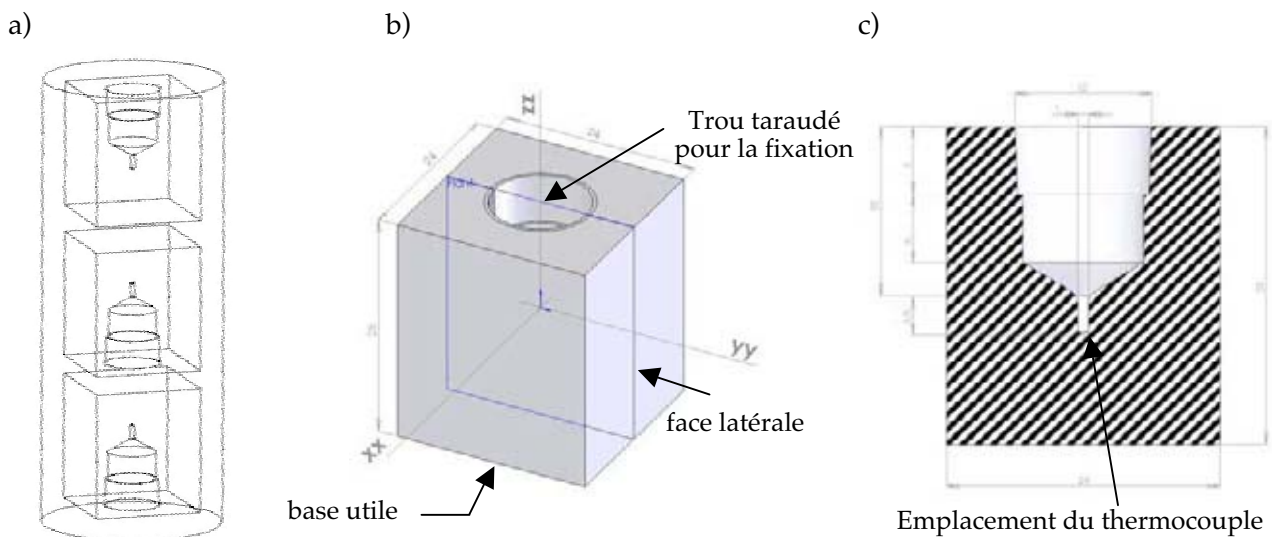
Prélèvement et géométrie des éprouvettes de corrosion isotherme :
